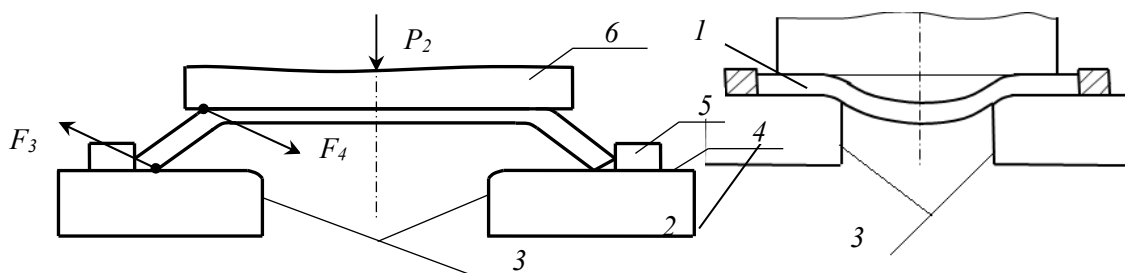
Нова схема самочинного формоутворення рифта (1 – заготовка; 2 – полка; 3, 4 – елементи матриці; 5 – фіксувальні планки; 6 – пуансон)
